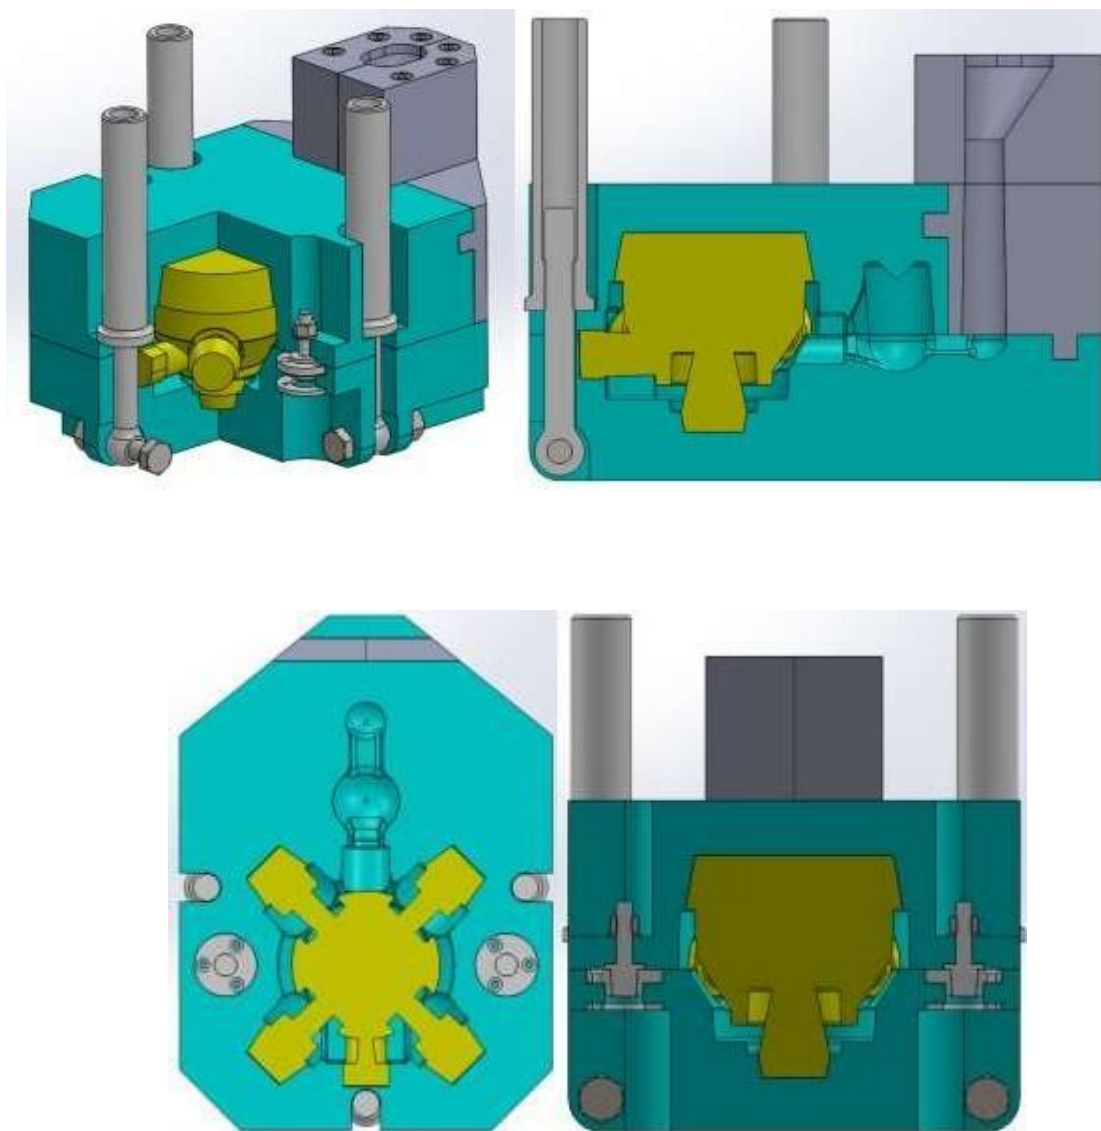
3D-модель кокіля для виготовлення підшипникового щита
